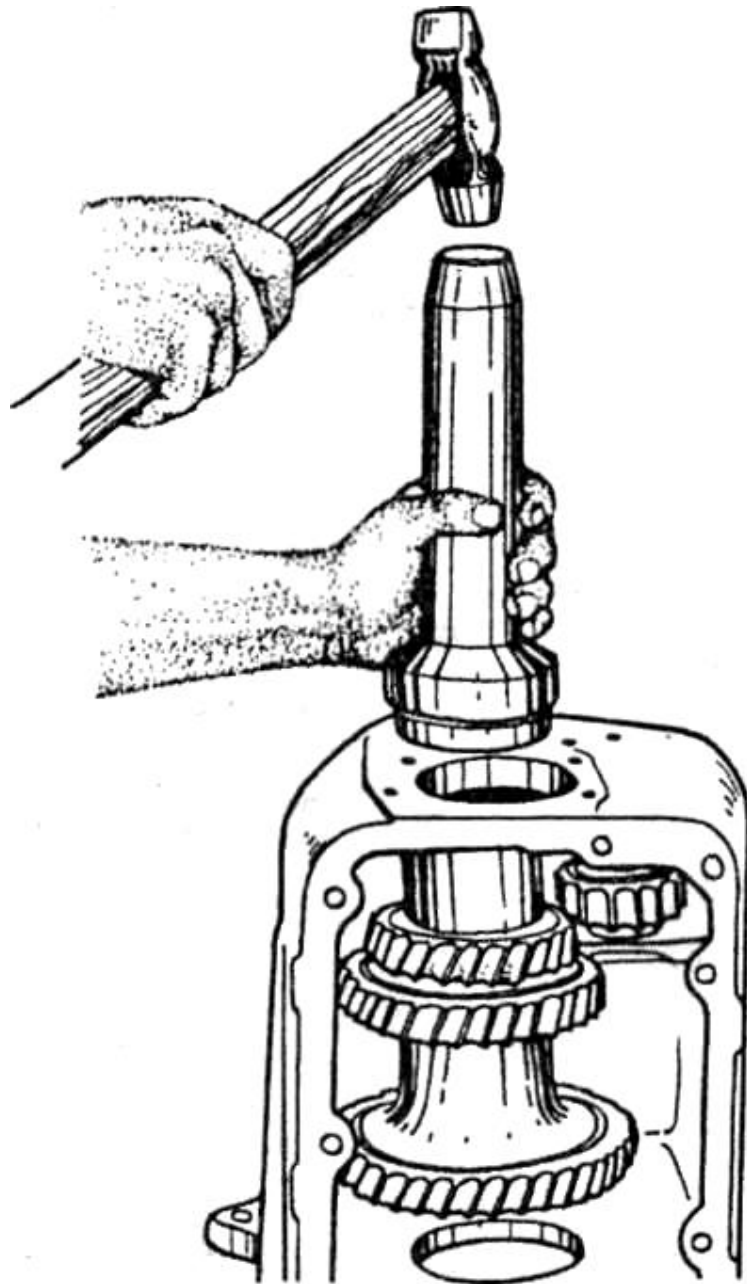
Напресування кулькового підшипника проміжного валу
